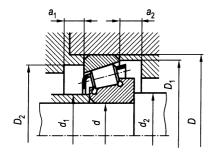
Установочные размеры для роликового радиально-упорного конического однорядного подшипника
